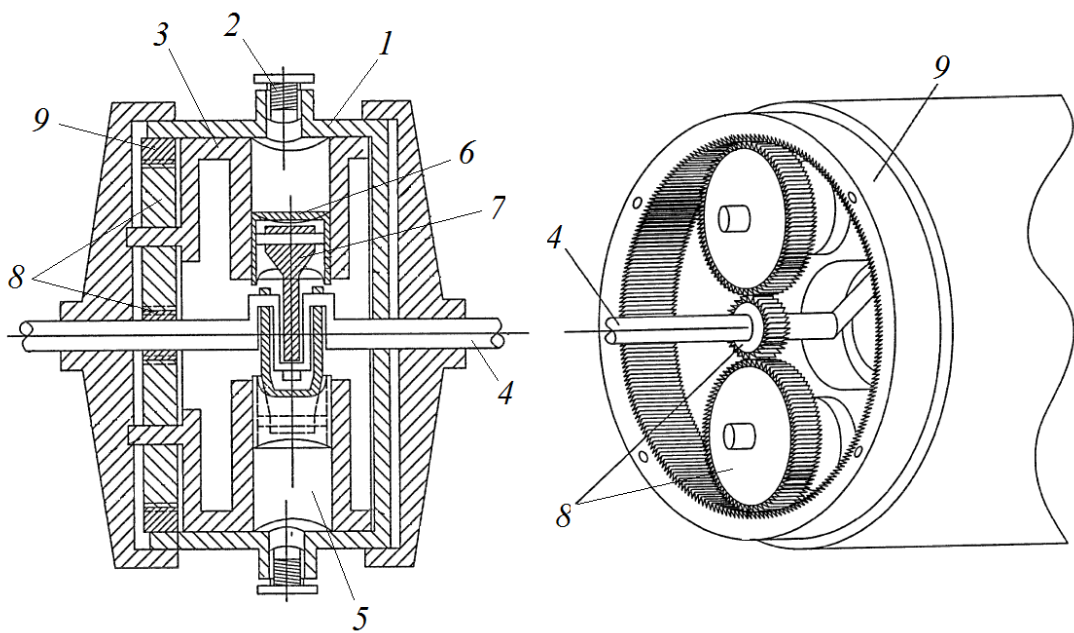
Загальна будова роторного двигуна барабанно-поршневого типу з рухомими камерами згоряння [125]: 1 – циліндричний корпус двигуна; 2 – компресійні втулки; 3 – рухомий барабан; 4 – колінчастий вал; 5 – робочий циліндр двигуна; 6 – поршень; 7 – шатун; 8 – блок шестерень; 9 – зубчастий вінець
